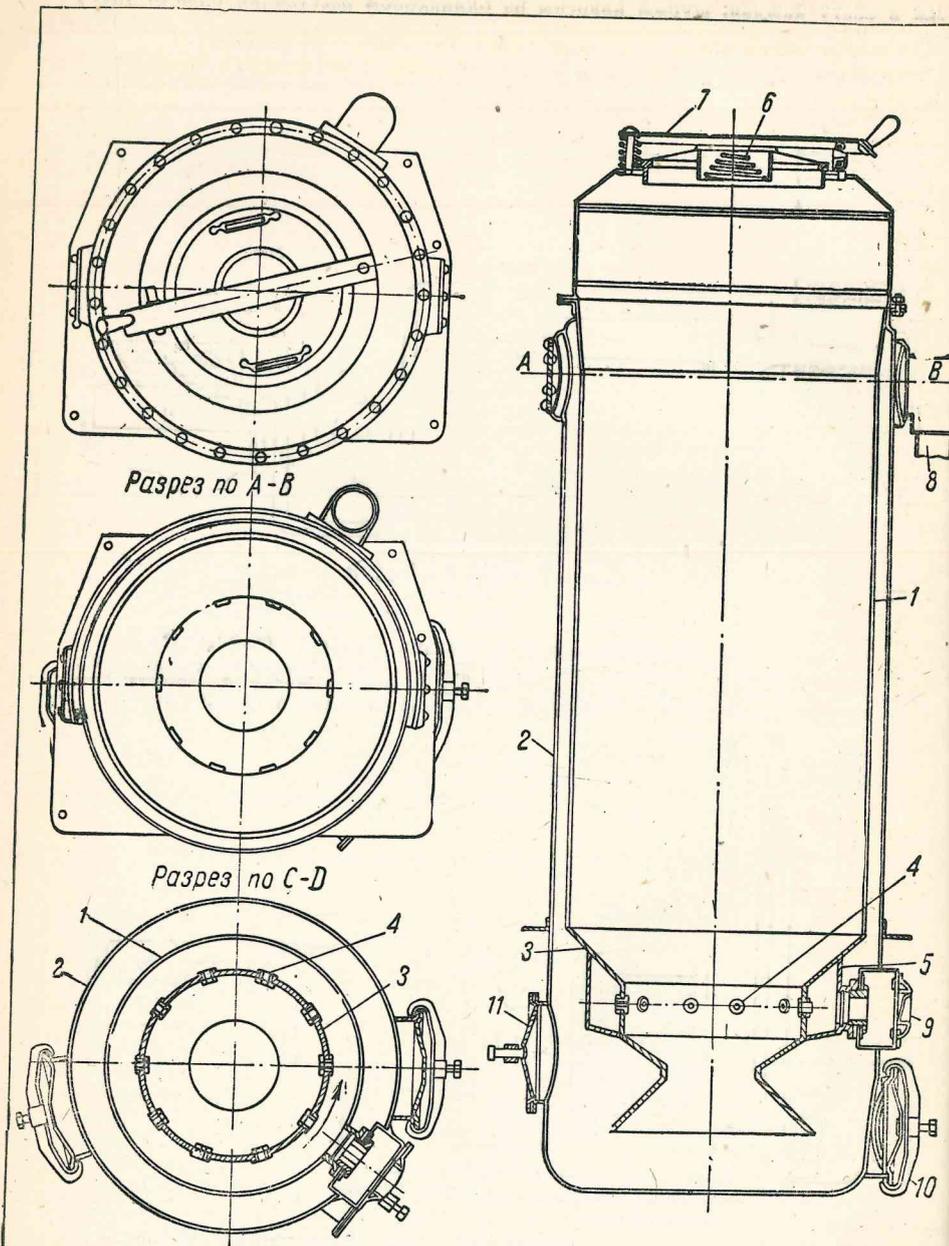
Схема газогенераторной установки „Имберт“ (тип „ОК“):
